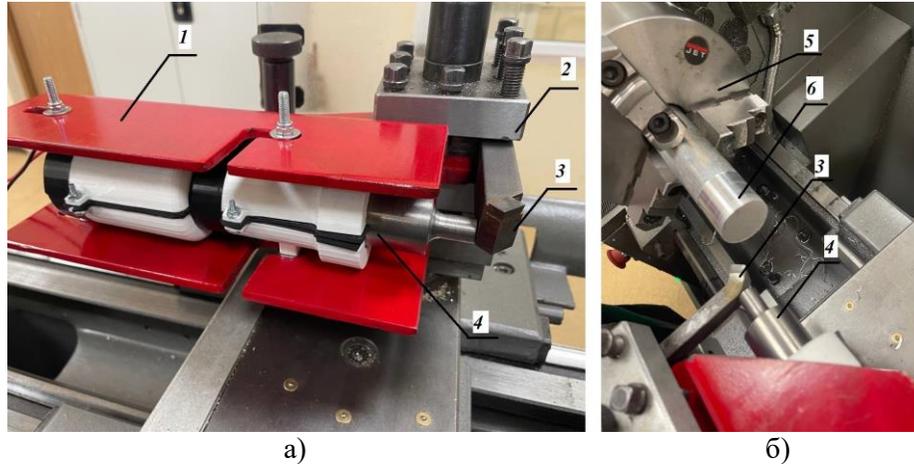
Экспериментальная установка на базе станка *JET GHB 1340A DRO*: а) 1 – приспособление для закрепления магнитострикционного преобразователя с возможностью регулировки угла закрепления; 2 – резцедержатель; 3 – резец; 4 – магнитострикционного преобразователя; б) 5 – трехкулачковый патрон; 6 – заготовка
